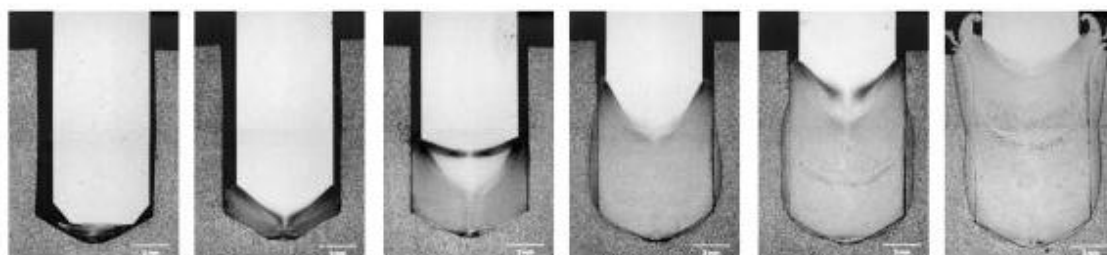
Escoamento do material do pino consumível durante a soldagem por fricção (MEYER 2001).
